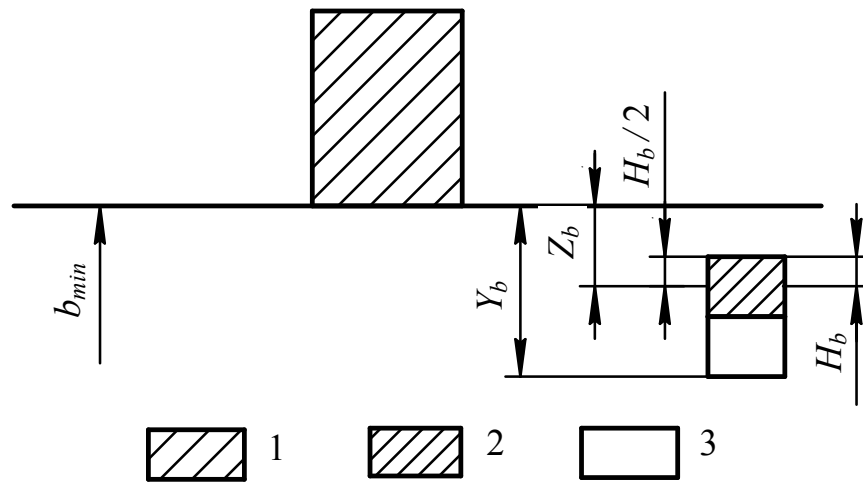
Поля допусків на ширину шліця: 1 - розміру b втулки; 2 - на виготовлення калібру-пробки; 3 - поле зносу калібру-пробки
